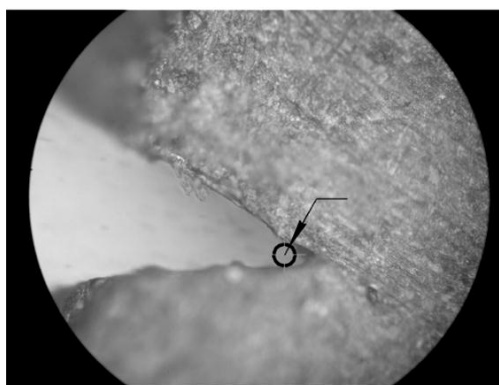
Фотография свинцового слепка режущей кромки ножа:
